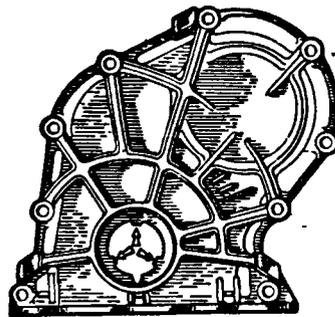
Крышка привода распределительного вала. Стрелками показаны выступы для центрирования крышки относительно ступицы шкива коленчатого вала
